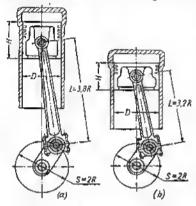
Dimensiones comparativas de un motor de émbolo de carrera larga (a) y de carrera corla (b)
